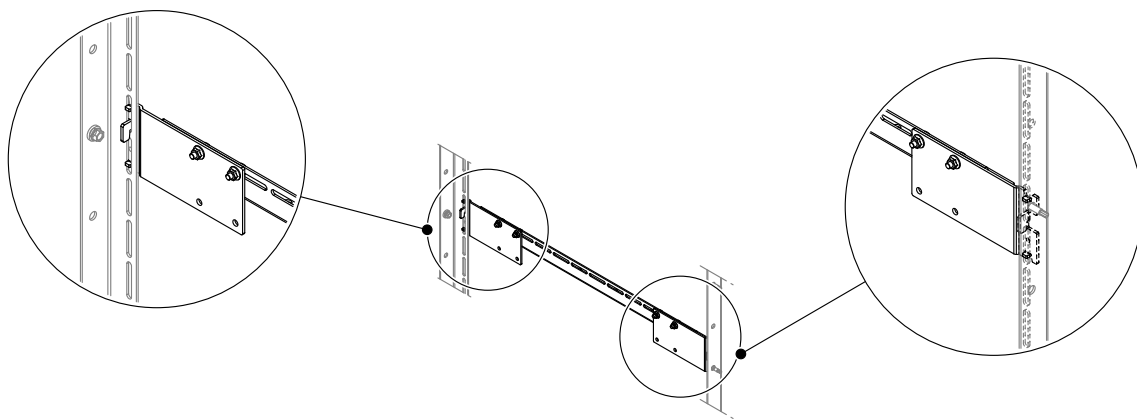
Montage des barres transversales pour montage de booster pour des installations d'une largeur allant jusqu'à 2100 mm
